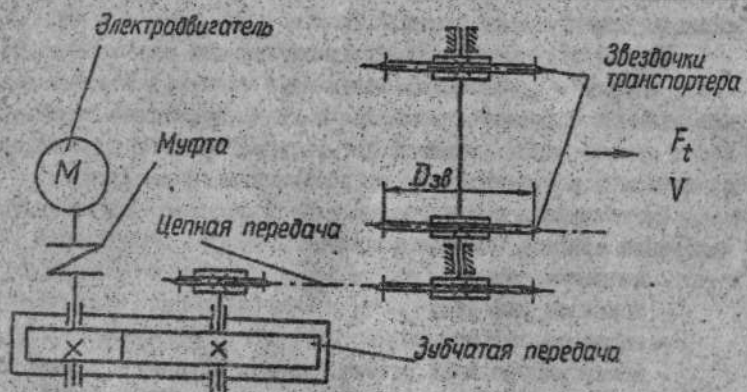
Схема привода цепного транспортера для загрузки и разгрузки самолетов
